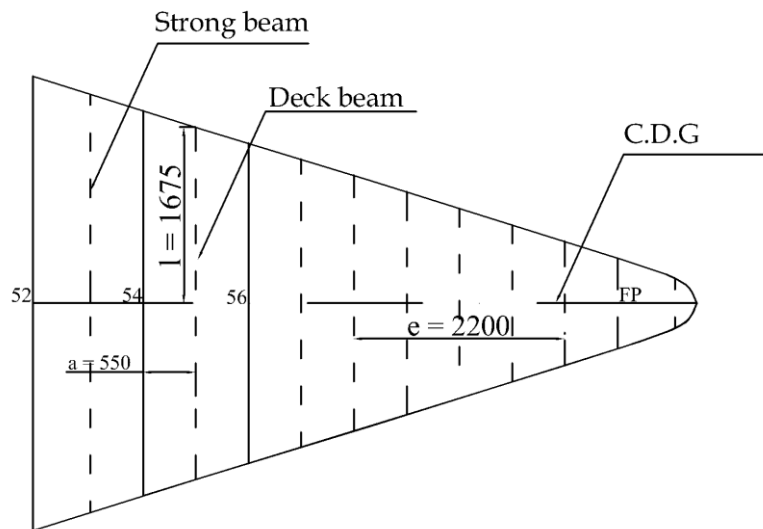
Jarak panjang tak ditumpu (l) pada deck beam kamar mesin, Tween Deck, bangunan atas dan rumah geladak
